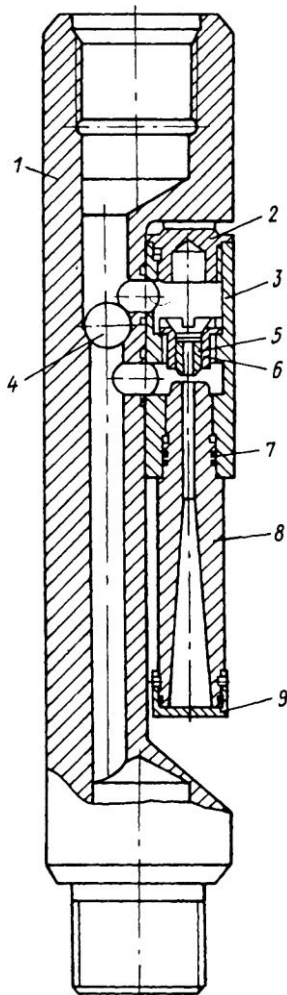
Пристрій для обробки свердловин УОС– 1:
